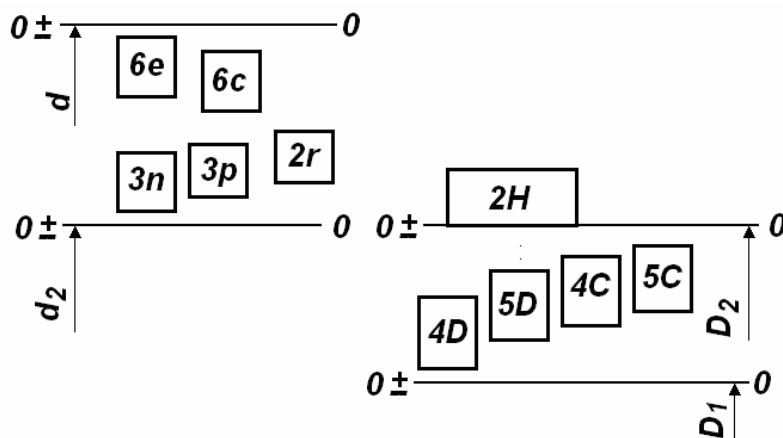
Розташування полів допусків нарізі з натягом.
